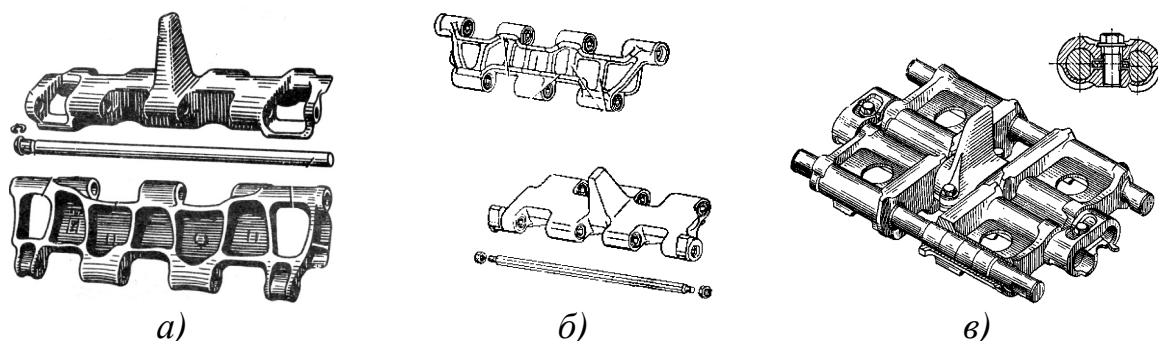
Траки: *а* – открытый металлический шарнир; *б, в* – резинометаллический шарнир
